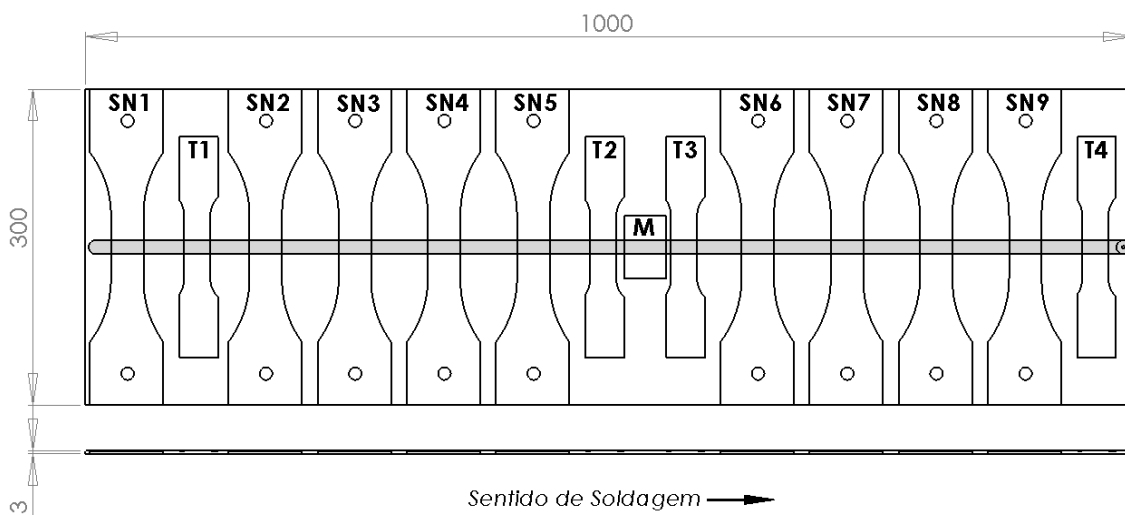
Disposição dos corpos de prova na chapa soldada.
